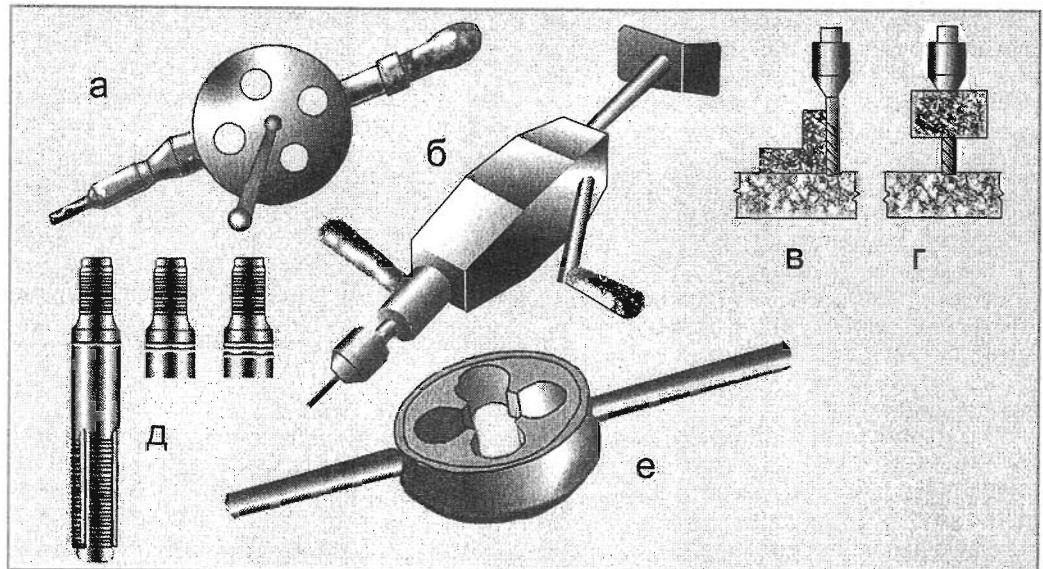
Ручные дрели: а – с открытой передачей; б – о закрытой передачей; в – использование угольника при сверлении; г – индикатор-ограничитель из корковой бутылочной пробки; д – метчики для нарезки резьбы; е – плашка для нарезки резьбы
